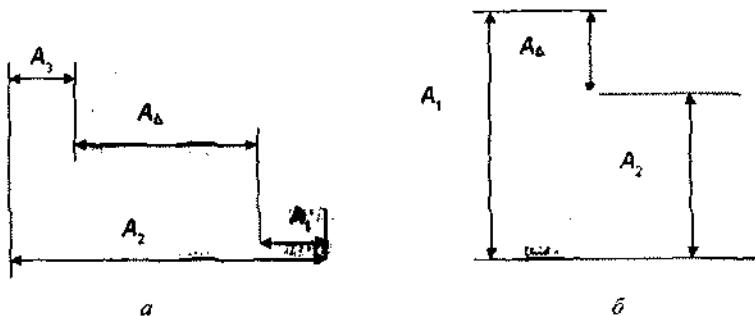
Схемы размерных цепей: а – детальная; б – сборочная
